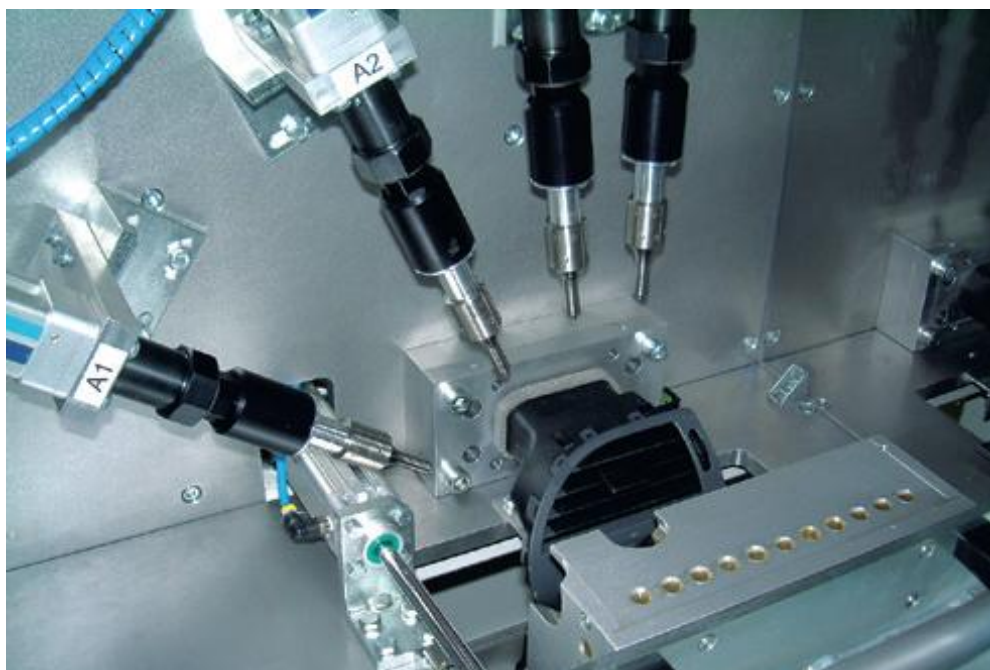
Техническое решение ультразвуковой сварки компании U-Sonic
